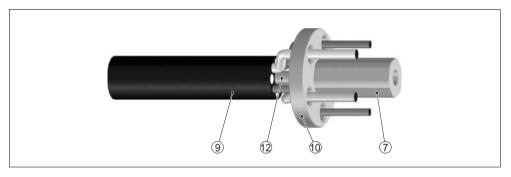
Cortar el cable de soporte (12) con el corta-pernos
